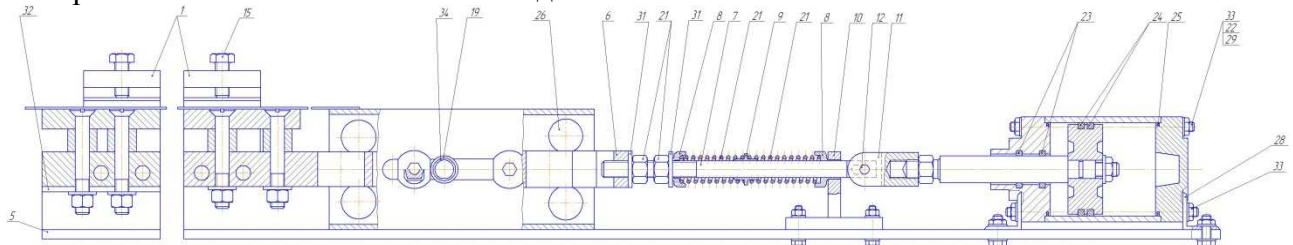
Экспериментальный сварочный модуль
